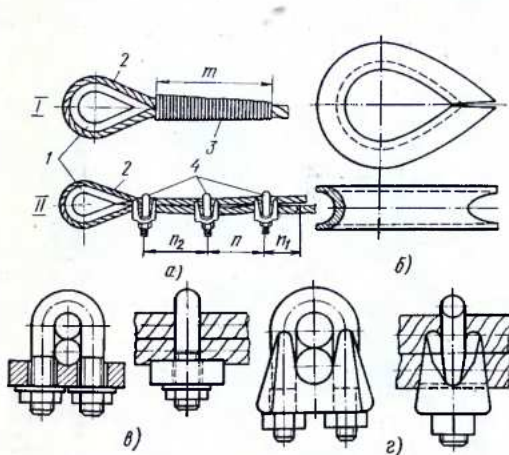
Крепление концов каната на коуше: а — общий вид крепления, б — коуш, в, г — обыкновенный и рожеквые болтовые зажимы; 1 — коуш, 2 — канат, 3 — обмотка, 4 — зажимы
